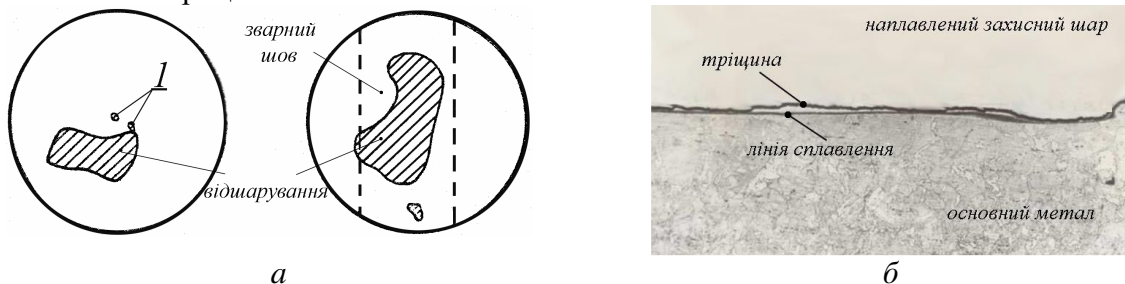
Карта УЗ-контролю зразків без зварного шва (зліва) та зі швом після випроб (а) і вигляд піднаплавкової тріщини (б) $\times 100$; I – дефекти, які виявлені під час УЗ-сканування зразків без зварного шва до наводнення і які не розвивалися після наводнення
